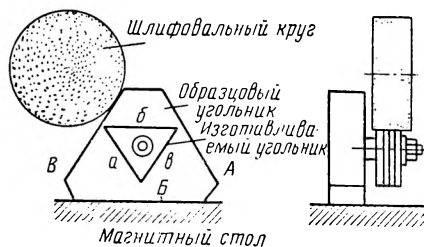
Схема установки для изготовления угольника с углом 60° с помощью образцового угольника
